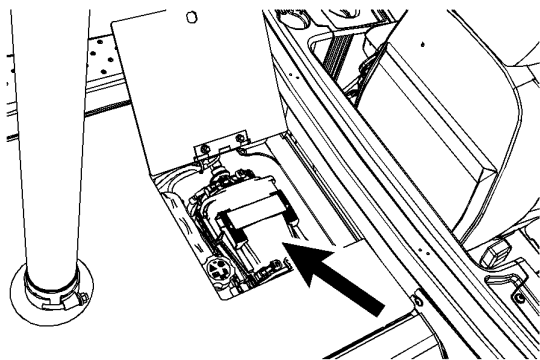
Место расположения воздушного фильтра двигателя. g06012618
